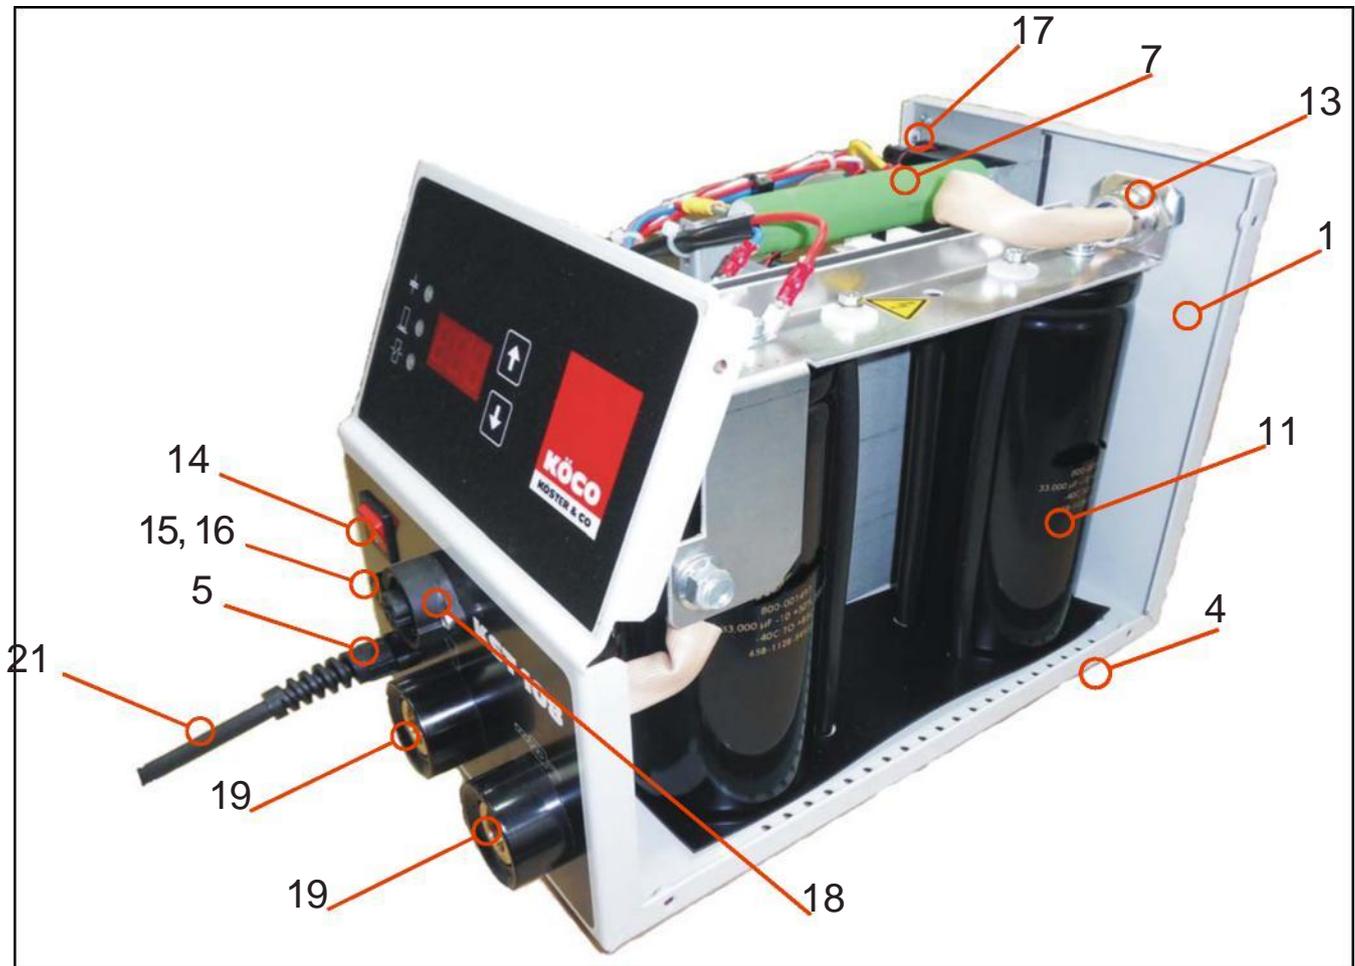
Rechte Seitenansicht hinten KST 108 bei demontierter Haube
